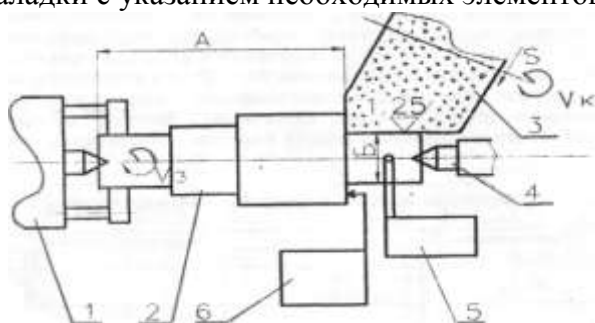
Схема наладки (1-поводковый патрон для вращения заготовки со скоростью V_3 ; 2- обрабатываемая заготовка; 3- режущий инструмент (шлифовальный круг); 4- задний центр, который в сочетании с передним центром патрона служит для базирования вала; 5- прибор активного контроля шлифуемого диаметра, который управляет движением подачи; 6- датчик для базирования вала в продольном направлении; А и Б - операционные размеры, которые необходимо получить в конце цикла обработки; V_k , V_3 , S_p - режимы резания)
